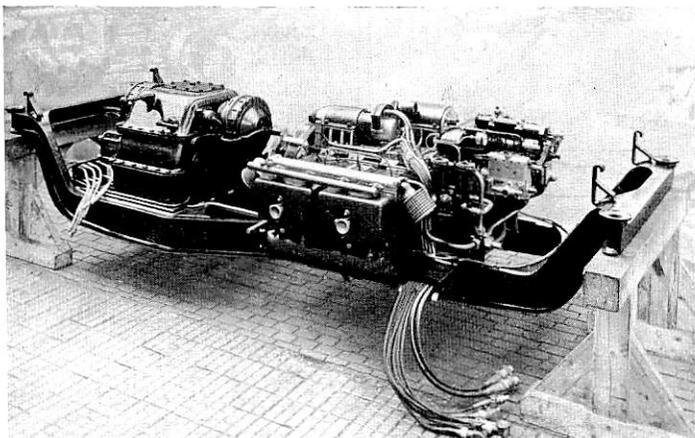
Motor- und Getriebetragrahmen des 180 PS-dieselmotormechanischen Triebwagens.
